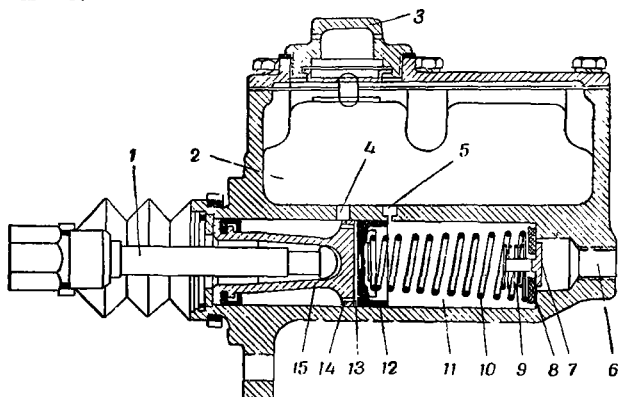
Главный тормозной цилиндр гидравлического привода тормозов (автомобиль ГАЗ-51)
